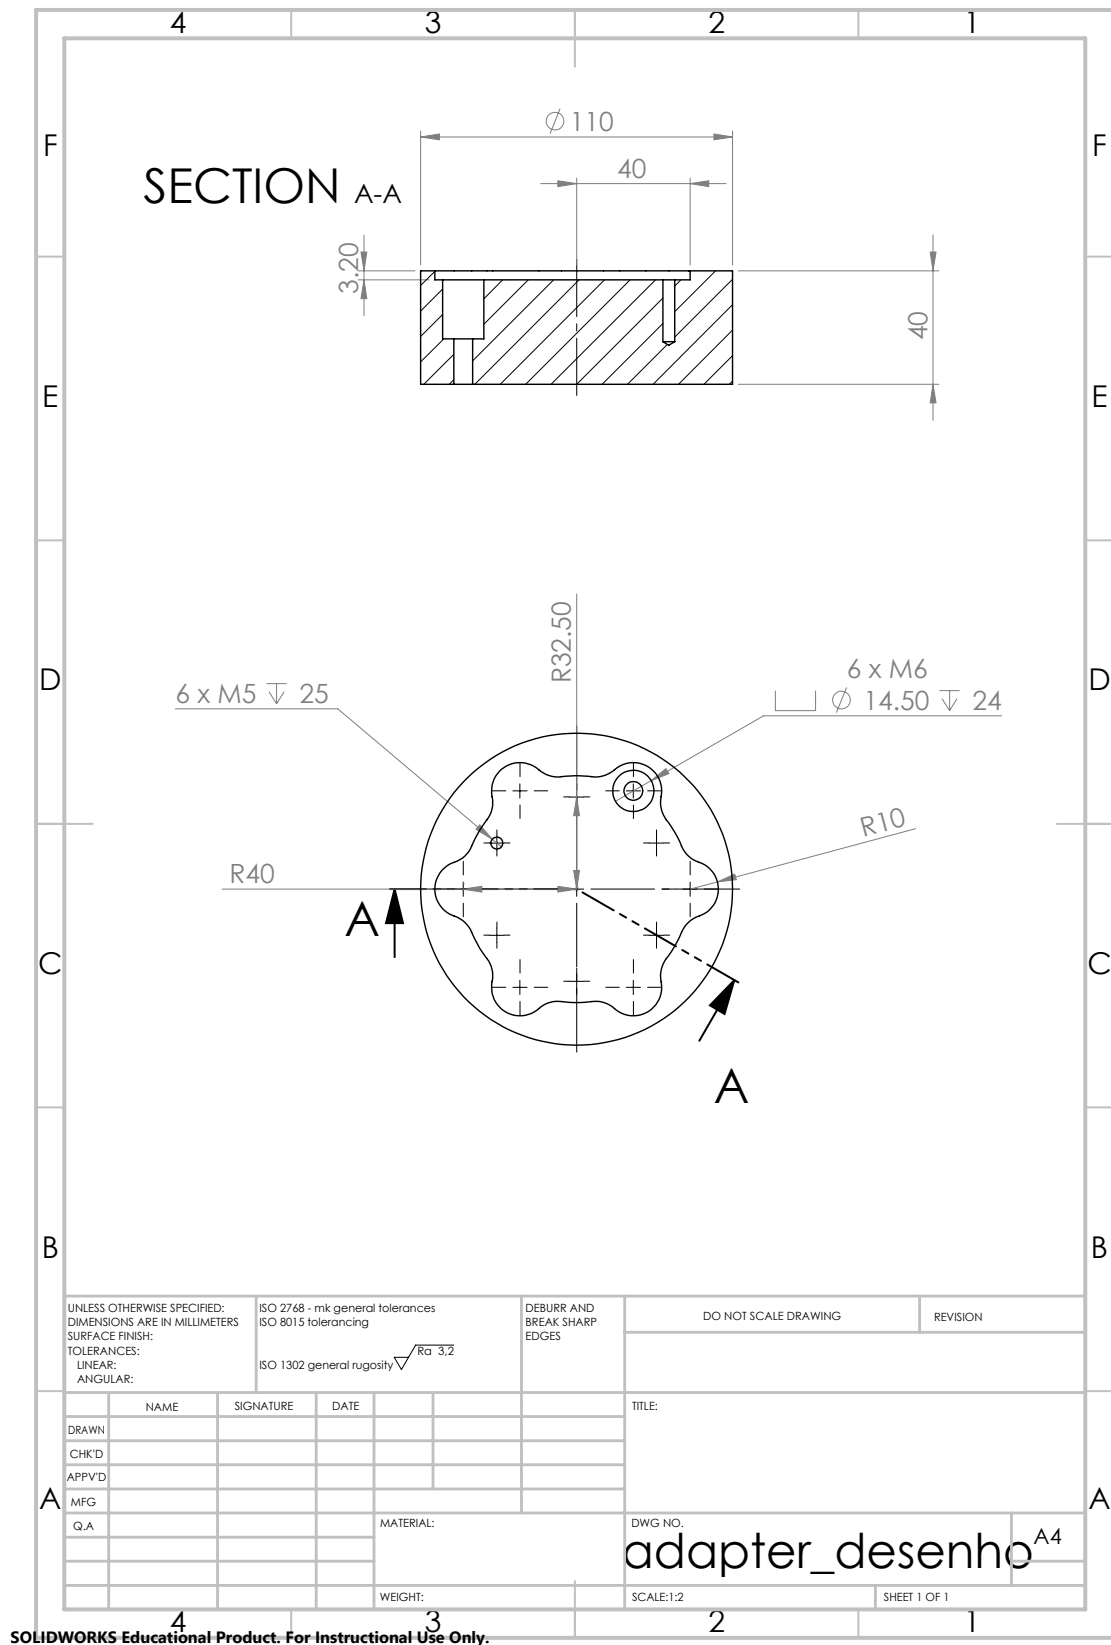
Desenho Técnico: Adaptador AFC-Troca de ferramenta
